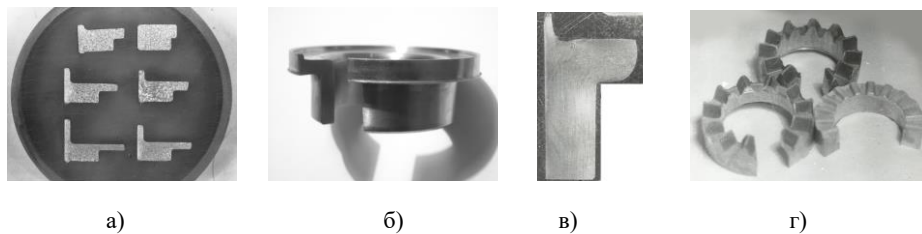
Загальний вигляд і перерізи заготовок, сформованих методами ШО за схемами прямого і зворотного витискування
